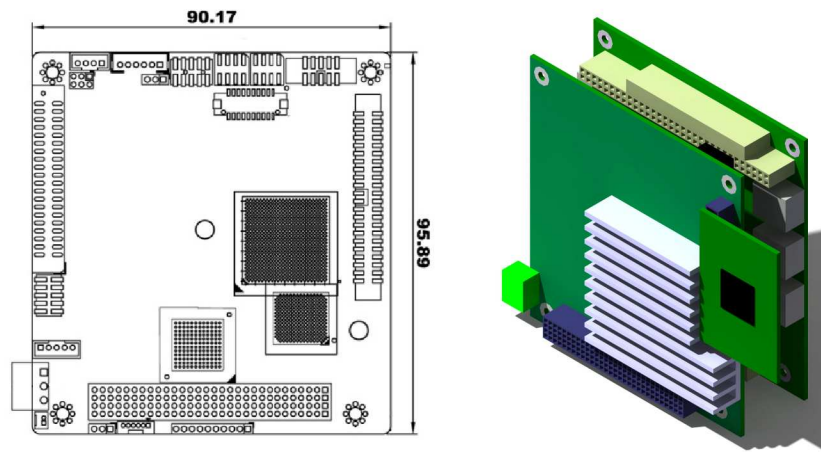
Dimensões do PC-104 e representação do módulo em CAD 3D.
